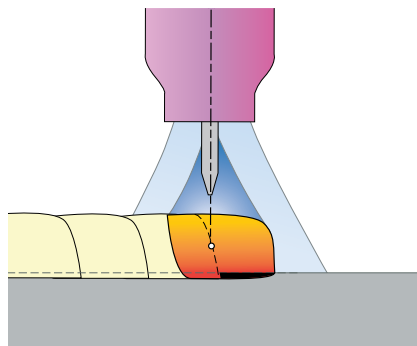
Наплавка горизонтальной поверхности в нижнем положении. Для снижения степени смешивания большая часть следующего валика укладывается на уже наплавленный валик. Только небольшая часть сплавляется с основным металлом.
